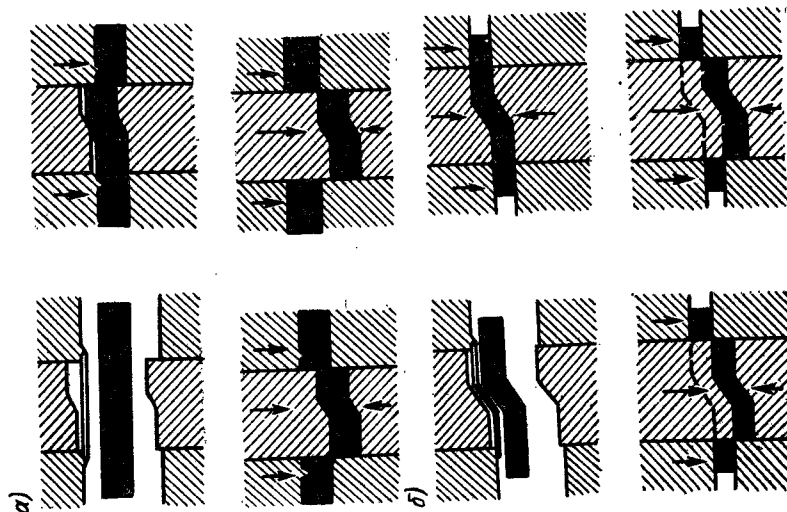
Изогнутые детали, получаемые чистовой вырубкой; а — из плоской заготовки; б — из изогнутой заготовки
